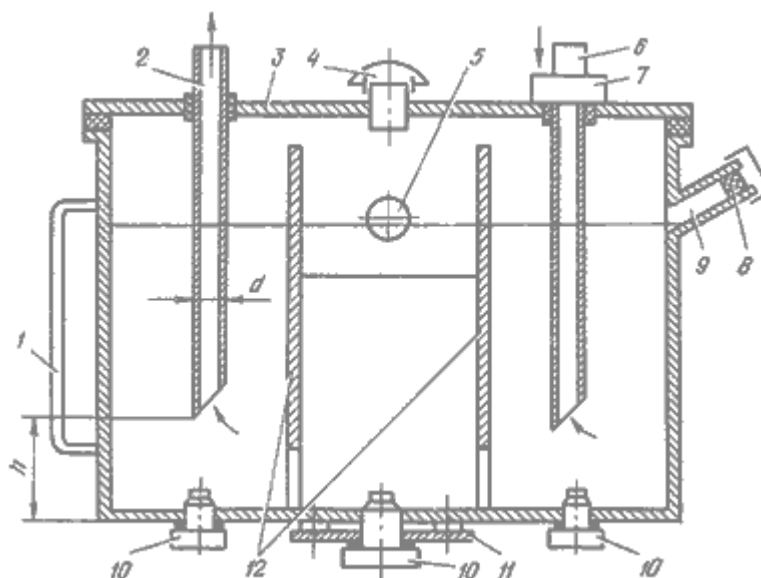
Гидробак: 1 - указатель масла; 2- всасывающая труба; 3 - крышка; 4 - сапун; 5 - глазок; 6 - сливная труба; 7 - фильтр; 8 - сетчатый фильтр (ячейки 0,1 0,1 мм); 9 - заливное отверстие; 10 - магнитная пробка; 11 - крышка для слива РЖ; 12 - перегородки (успокоители)
